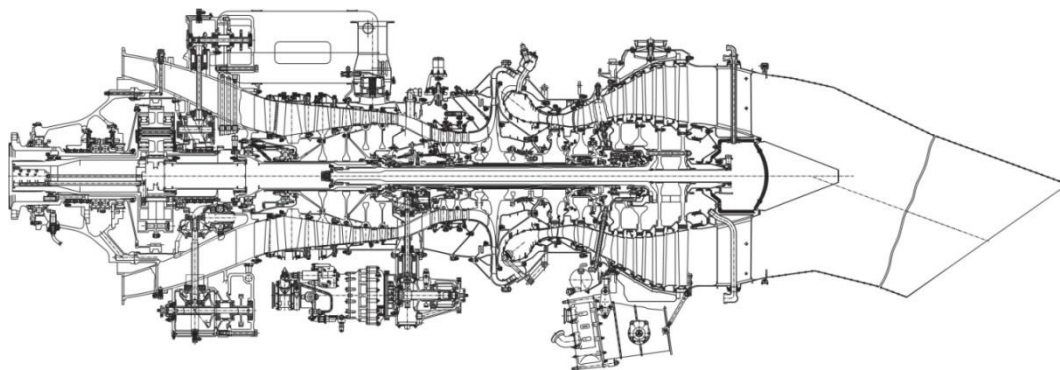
Principiální schéma turbovrtulového motoru PT6 s tandemovými rotory
